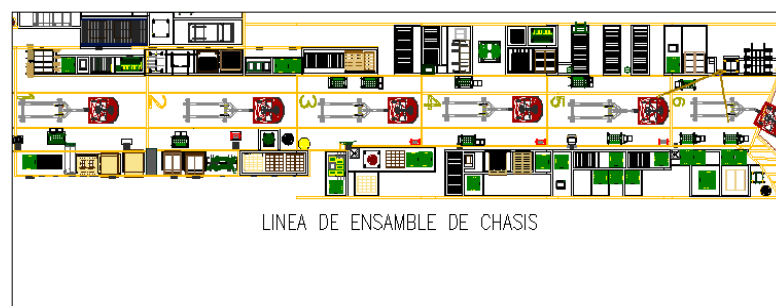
Línea de ensamble de chasis (Cortesía John Deere)
